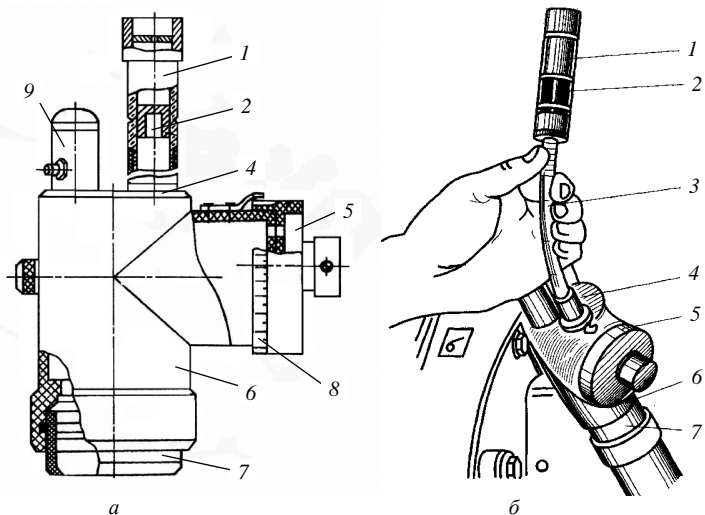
Устройство индикатора КИ-13671 (а) и измерение расхода картерных газов индикатором КИ-13671 (б): 1 – сигнализатор; 2 – поршень сигнализатора; 3 – удлинитель; 4 – патрубок; 5 – крышка; 6 – корпус; 7 – переходник; 8 – шкала; 9 – колпачок
